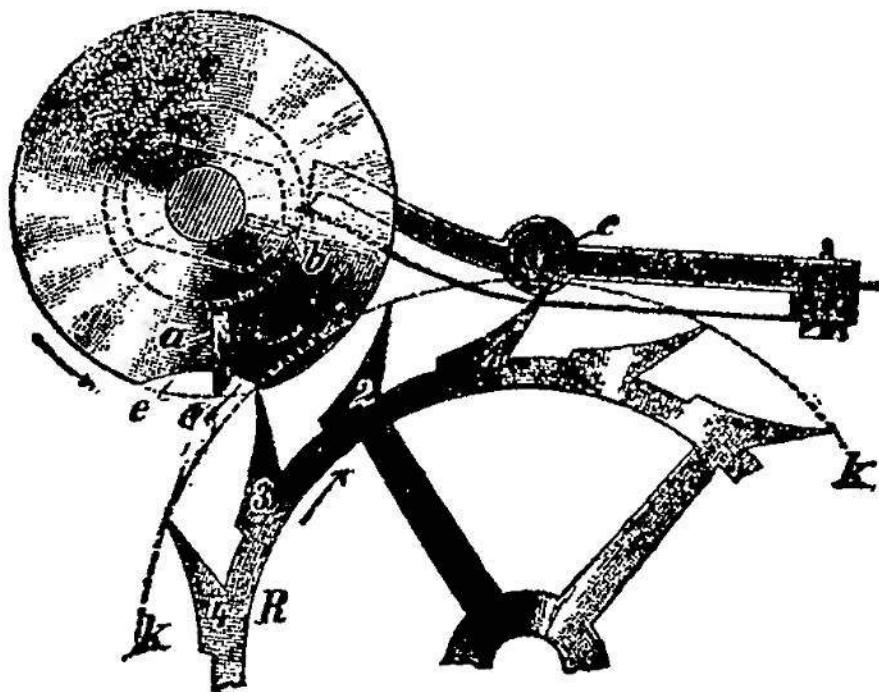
Прескакивание зубцов спускового колеса в хронометре.
